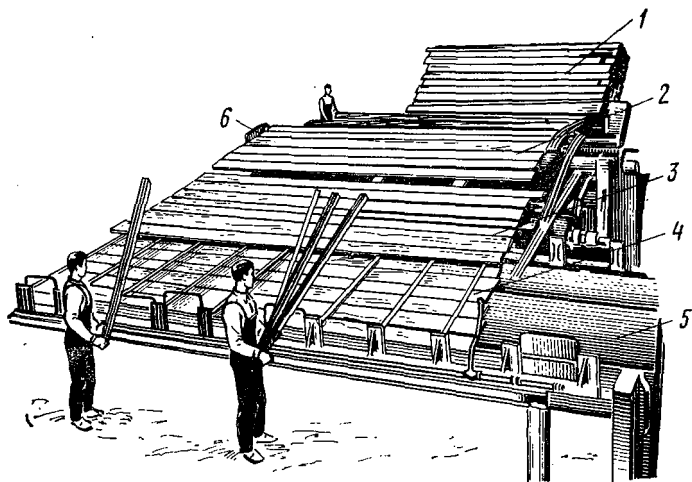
Штабелеукладчик с ручной раскладкой прокладок: 1 — наклонный подъемник, 2 — подборочный горизонтальный стол, 3 — вспомогательный стол, 4 — формируемый штабель, 5 — платформа вертикального подъемника, 6 — устройство для выравнивания торцов досок
